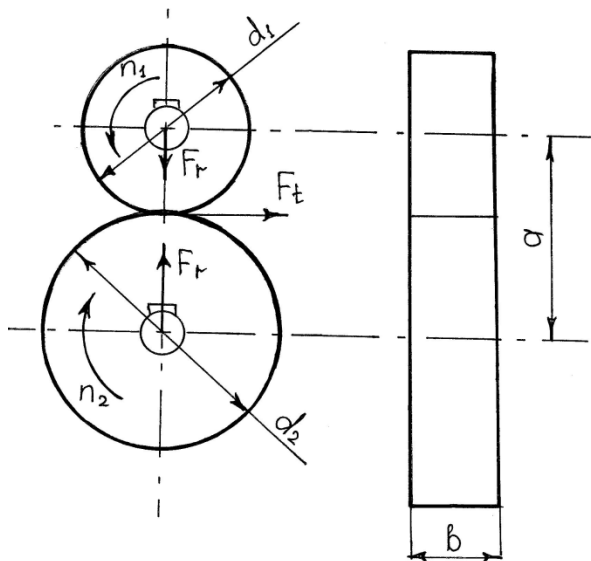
Схема циліндричної фрикційної передачі
